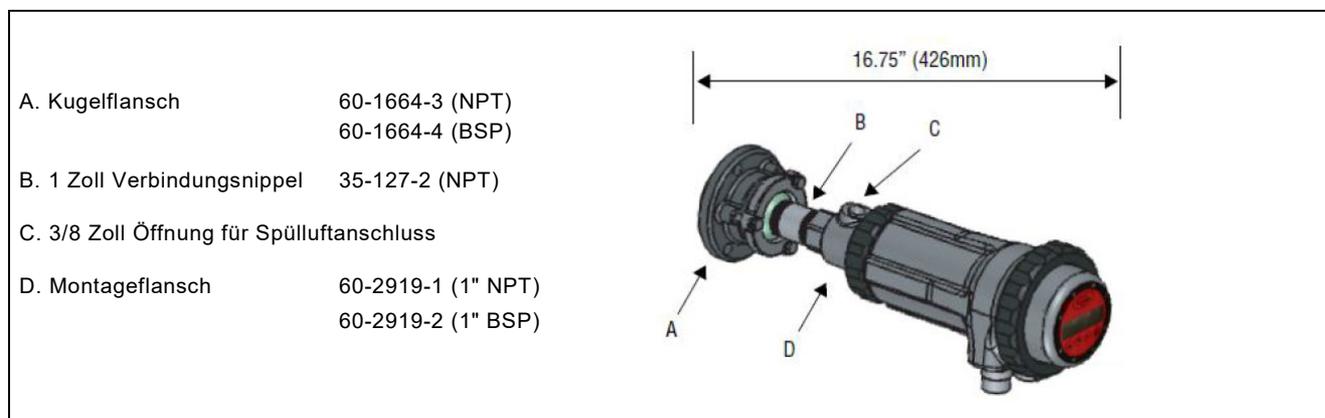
Kugelflansch, Flammenwächterkabel und Überdruckkupplung
